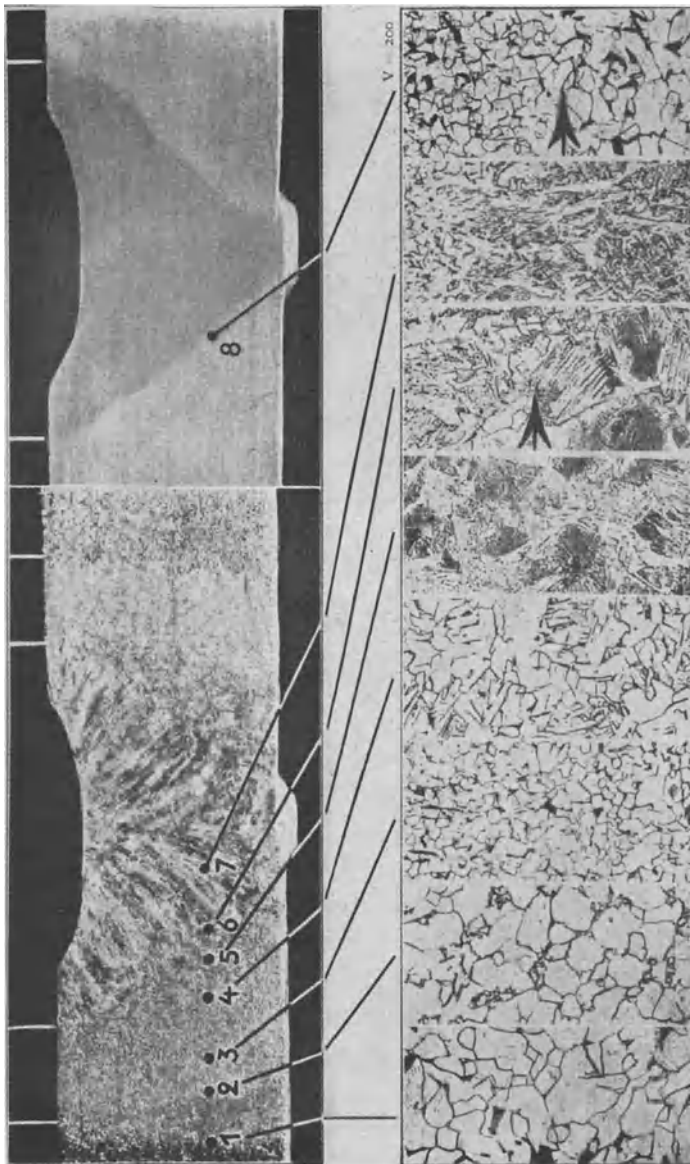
Gefügeaufbau einer Lichtbogenschweißung mit Manuelektrode.
